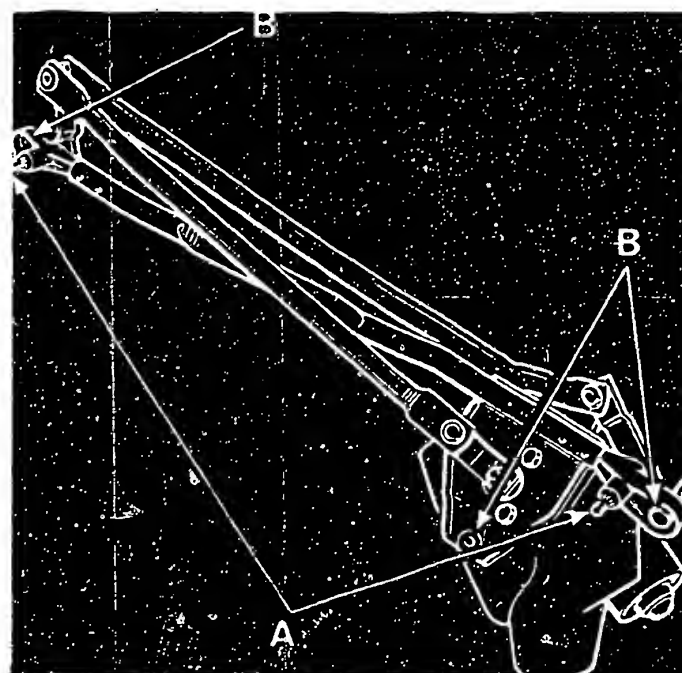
Befestigungsschrauben des Scheibenwischer-Mechanismus (B)
